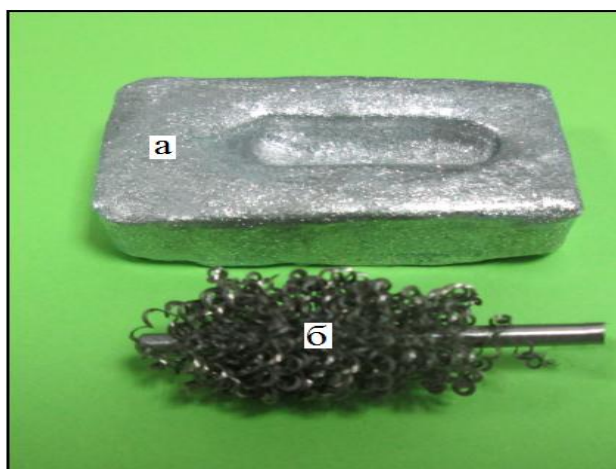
Процесс изготовления дренажа: а - пресс-форма; б – заготовка
